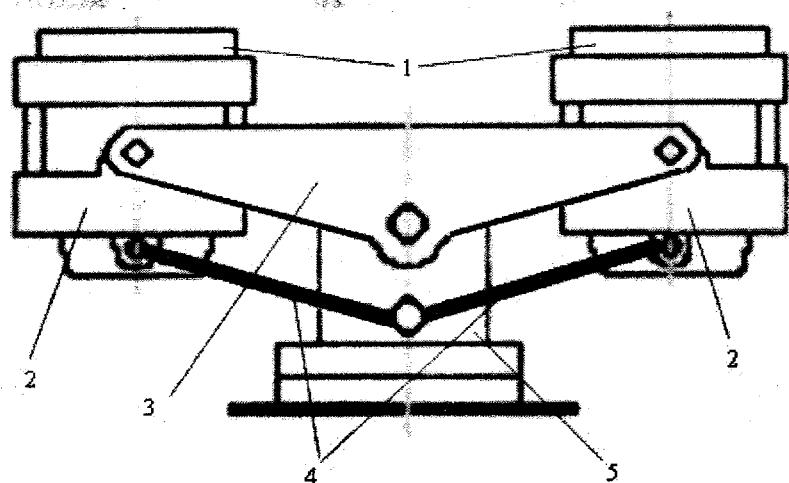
Схема подъёмно-поворотного сталеразливочного стенда:
